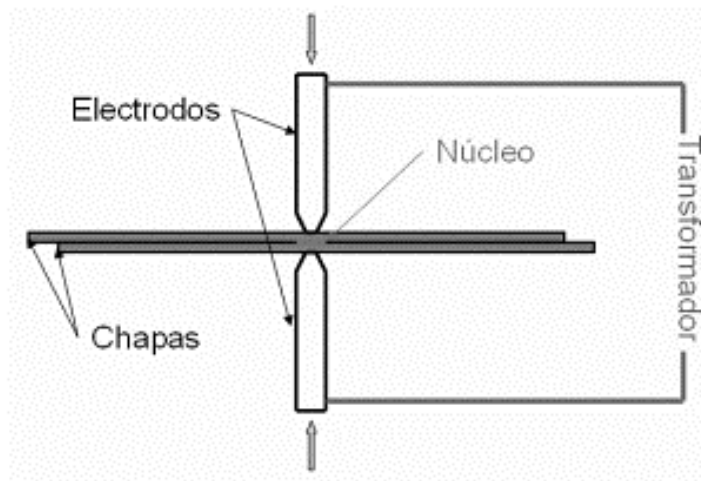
Sistema de soldadura por punto (MG, 2022).
